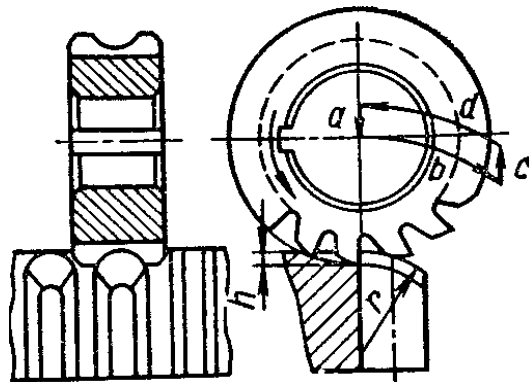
Схема закругления торцов зубьев дисковой фасонной фрезой
